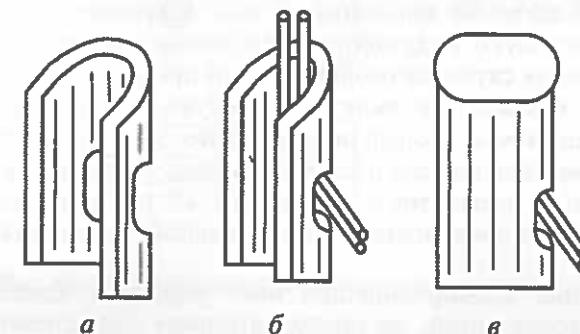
Получение контактного соединения при электромонтаже сваркой:
